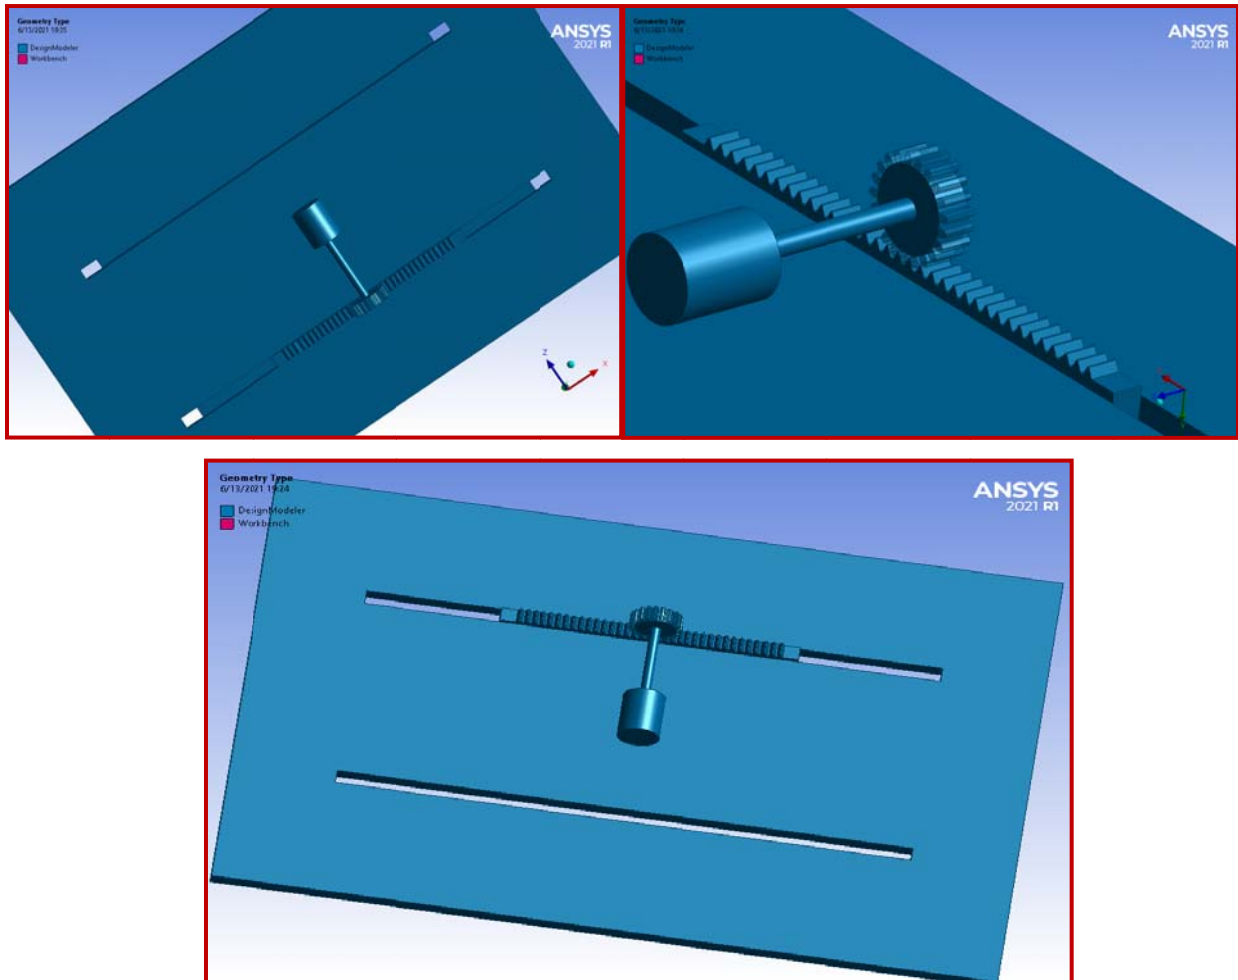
Vue d'ensemble chariot-moteur-engrenages.
